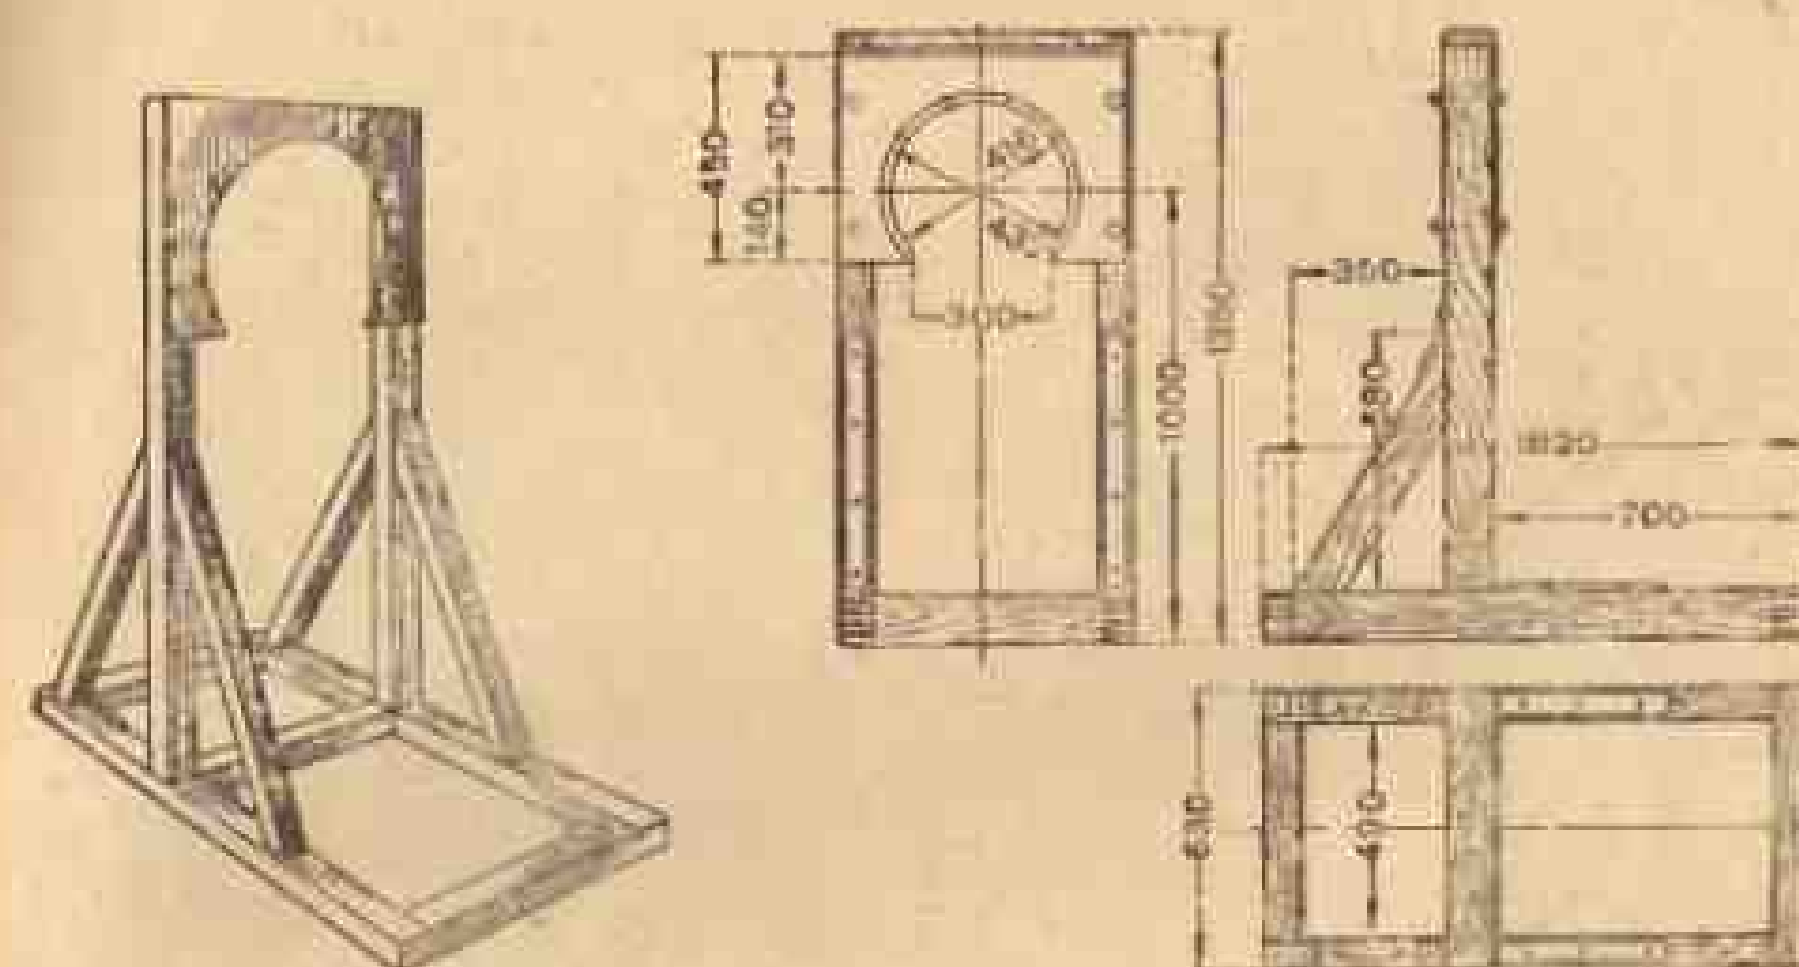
Стойка для разборки, сборки и регулировки мотора
